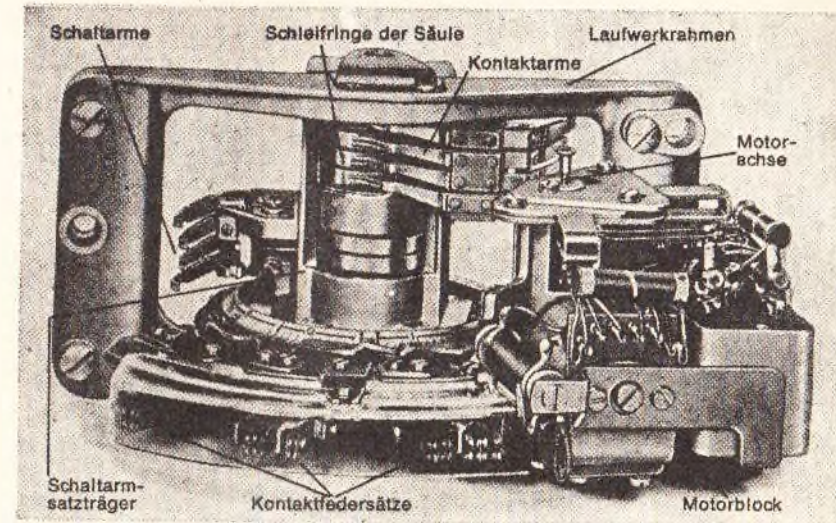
Frontansicht eines vierarmigen EMD-Laufwerks
